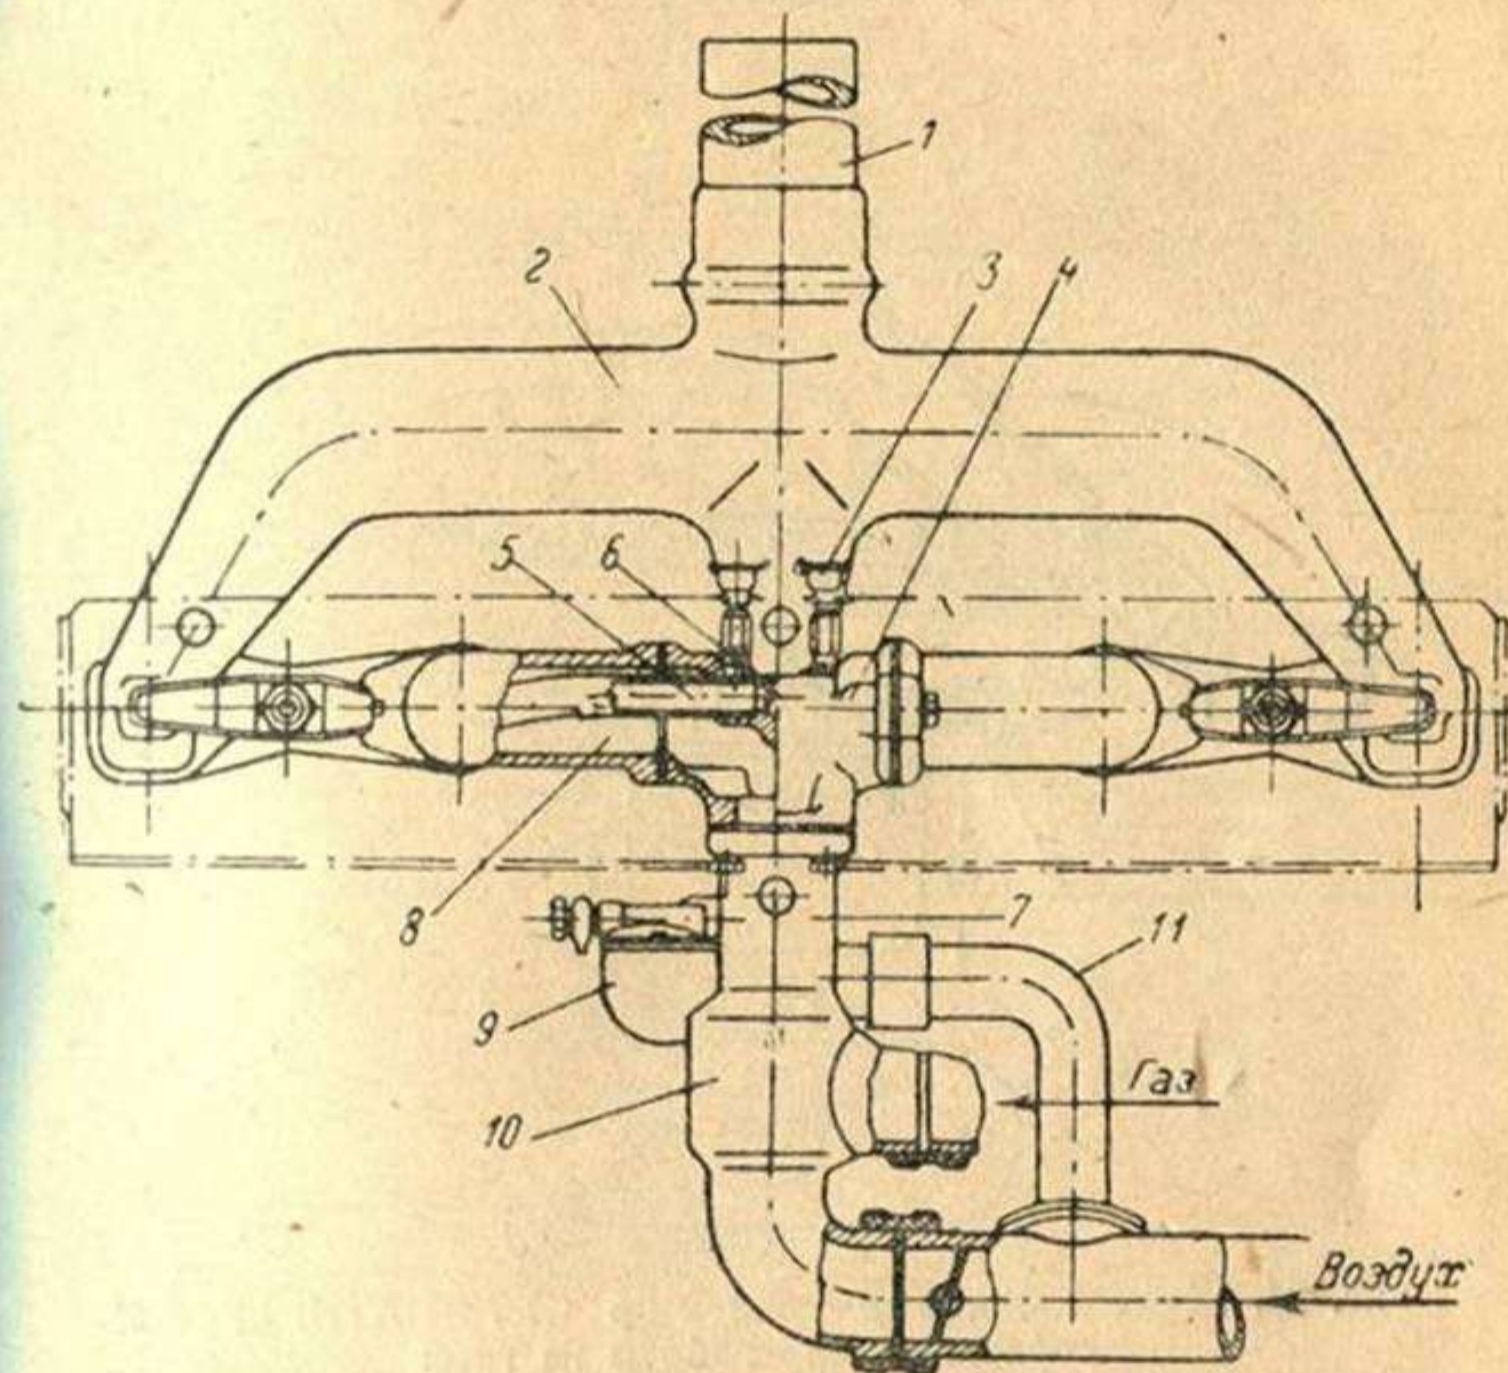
Выхлопной и всасывающий коллекторы газового двигателя СХТЗ-НАТИ:
